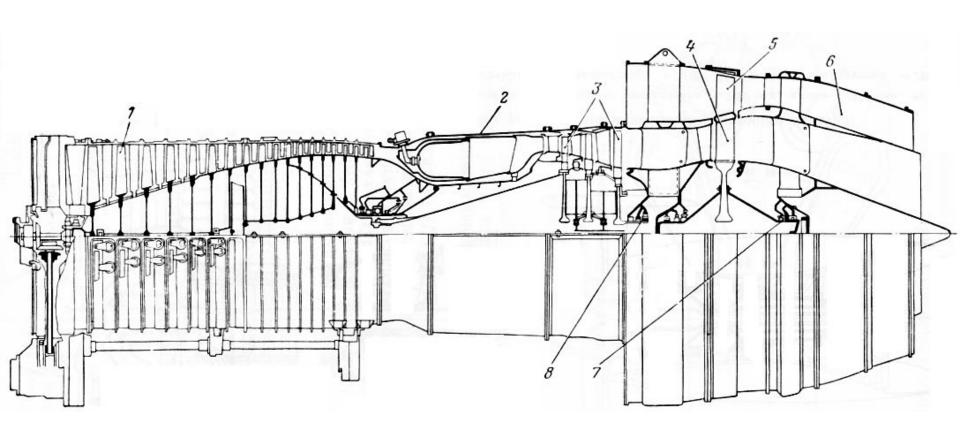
а. Схема ДТРД с задним расположением вентилятора второго контура: 1 – 17-ступенчатый компрессор; 2 – камера сгорания; 3 – трехступенчатая турбина; 4 – турбина турбовентиляторной приставки; 5 – вентилятор турбовентиляторной приставки; 6 – воздушный контур турбовентиляторной приставки; 7,8 – задний и передний подшипники турбовентиляторной приставки.
